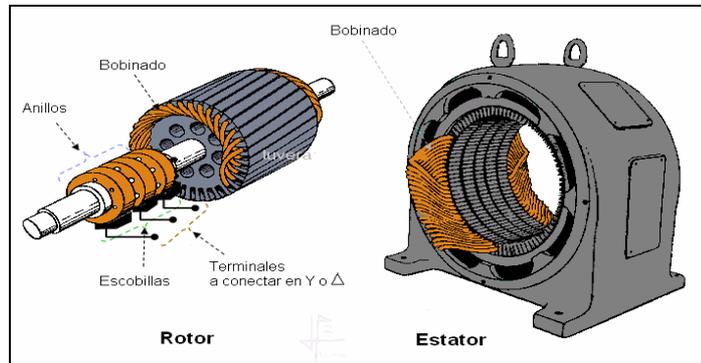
Rotor y estator de un motor de inducción de rotor devanado.
